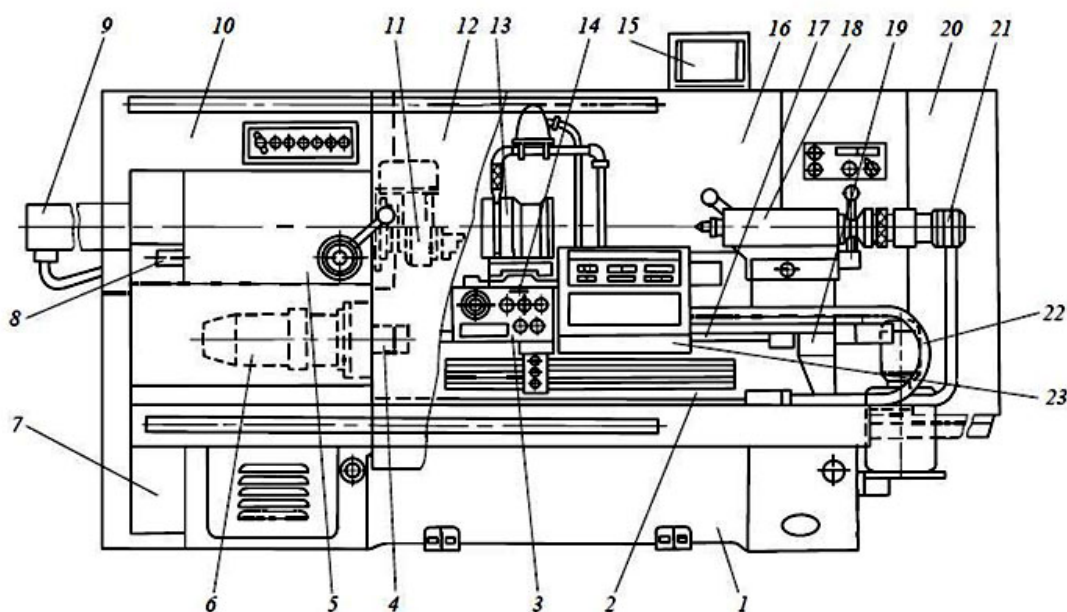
Токарный станок с ЧПУ 16К20Ф3
